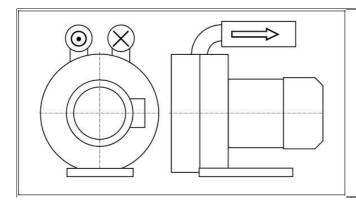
Двухпоточная конструкция вакуумного насоса/компрессора с двумя рабочими колесами.
